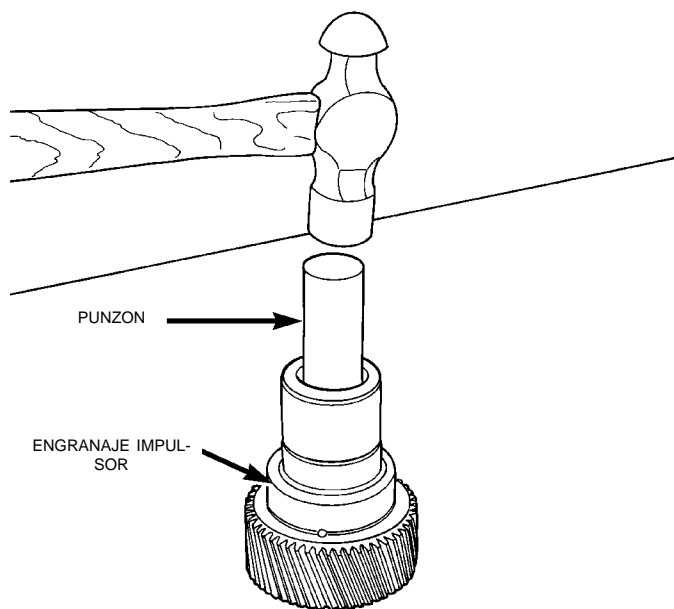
Retiro del cojinete de guía del engranaje impulsor
